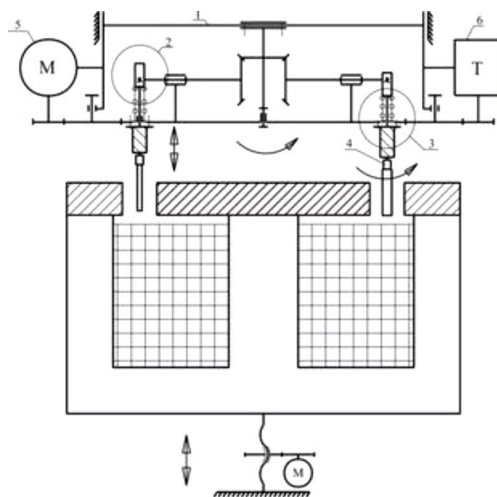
Кинематическая схема установки для МАП компрессорных лопаток:
